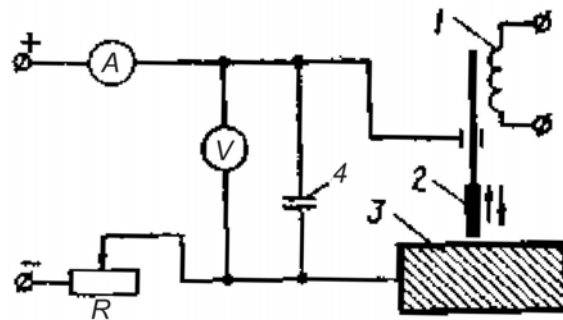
Принципова схема установки для електроіскрового нарощування деталей:
